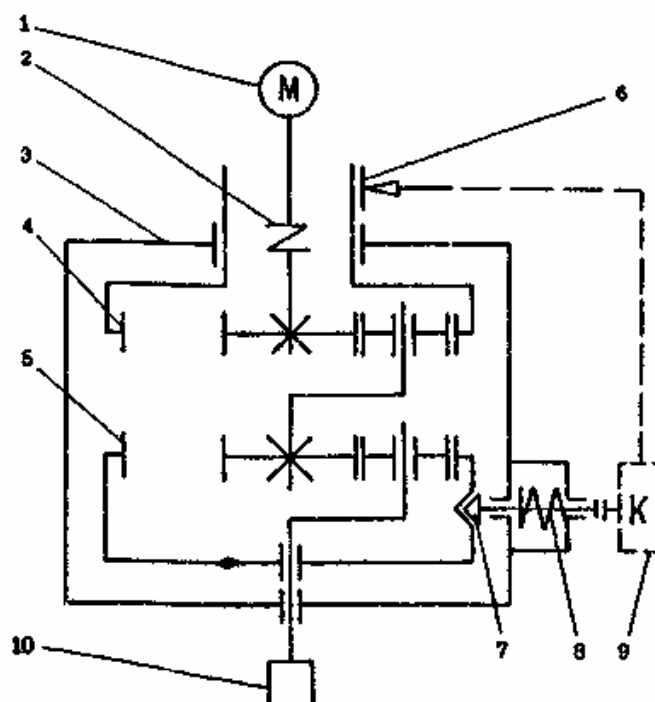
Схема электромеханического гайковерта: 1 – электродвигатель; 2 – муфта; 3 – корпус; 4 и 5 – колеса корончатые; 6 – тормоз колодочный; 7 – конический стержень; 8 – пружина; 9 – конечный выключатель; 10 – шпиндель
